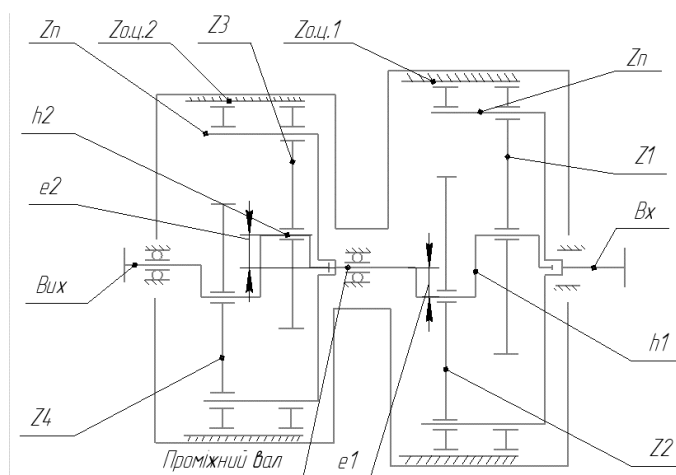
Кінематична схема 2-х ступінчатого планетарно-цівкового редуктора
